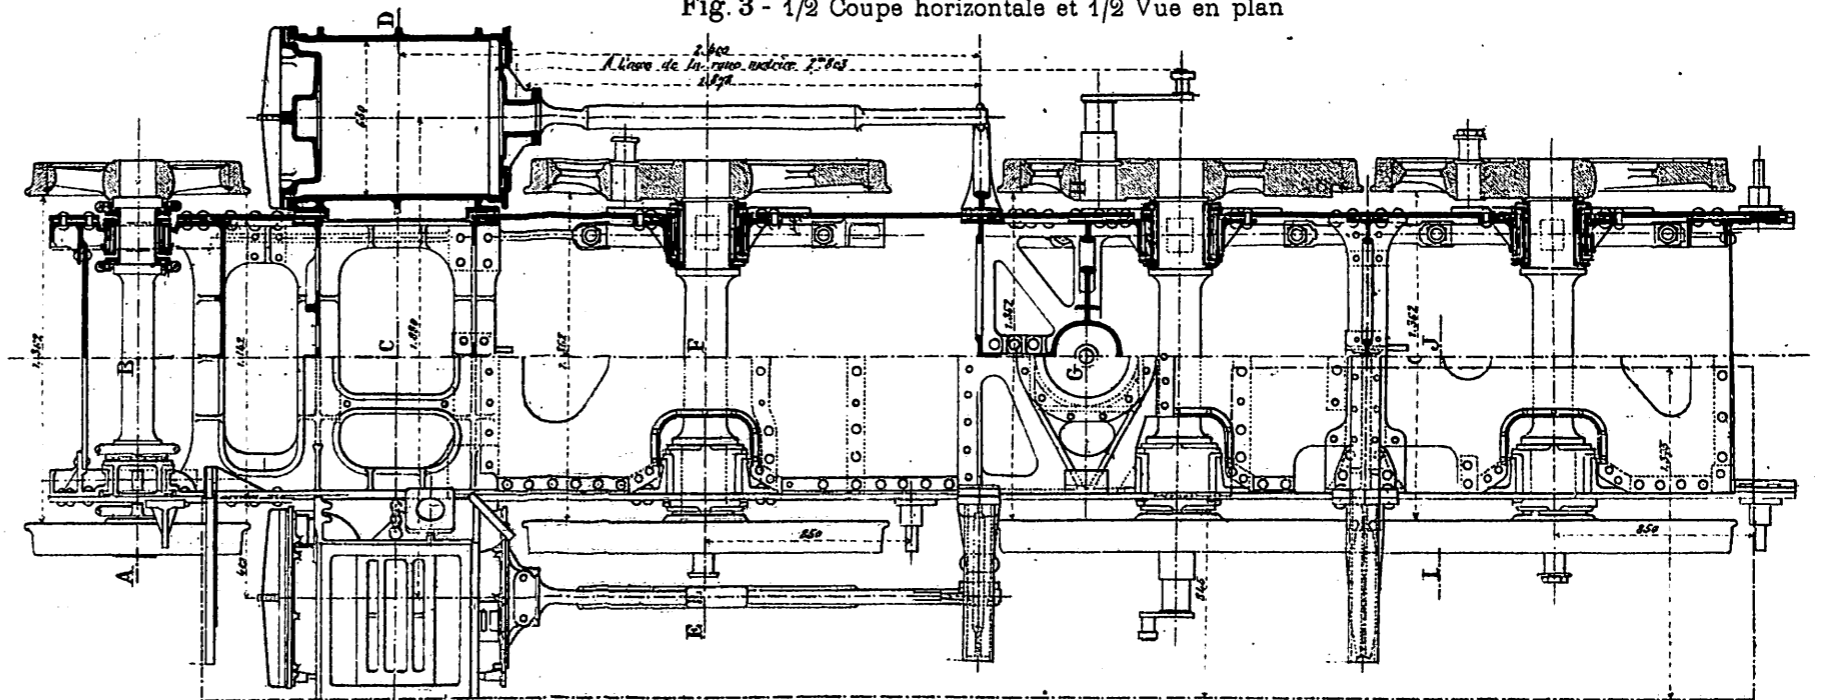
1/2 Coupe horizontale et 1/2 Vue en plan
